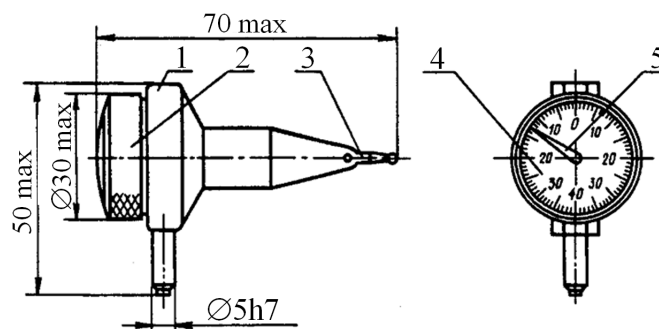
Внешний вид и основные размеры рычажно-зубчатых индикаторов типа ИРТ:
